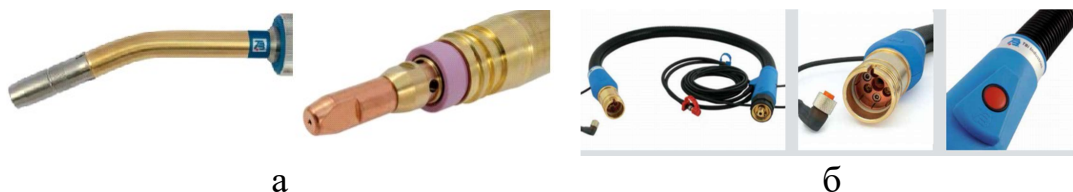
Роботизированная сварочная горелка TBi RM42G (а); шланговый пакет TBi RoboMIG (б)
